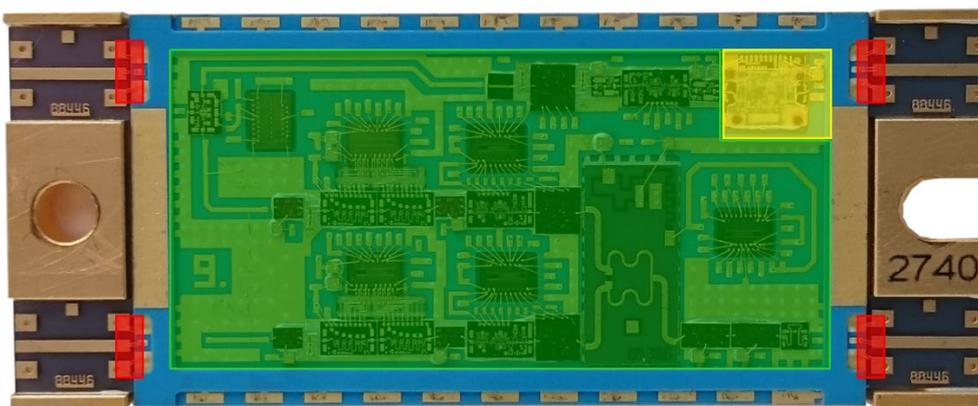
Области автоматической разварки МИС СВЧ и поликоровых плат.
